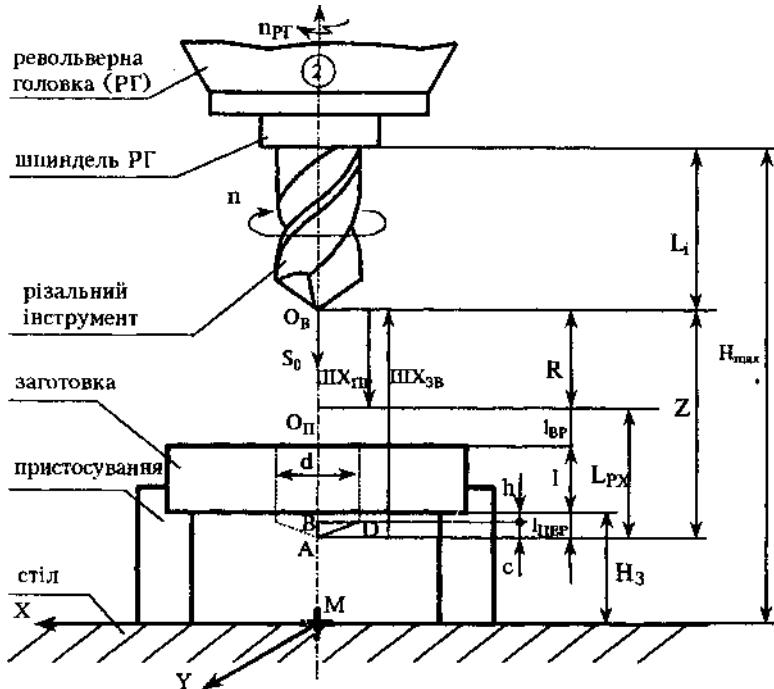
Схема взаємного розташування стержньового мірного інструменту (свердла) та заготовки при обробці отвору  $0d$
